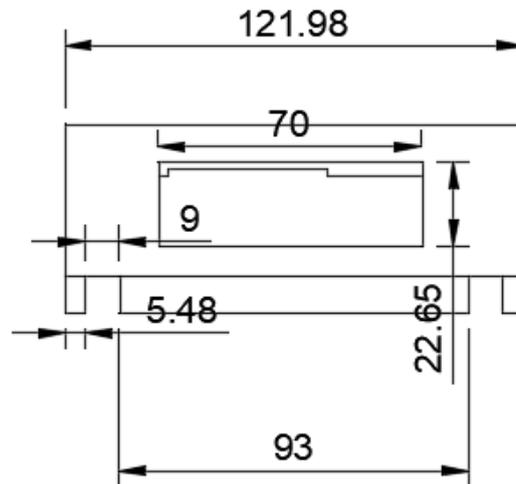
Medidas de la vista frontal, parte superior del diseño en 3D
